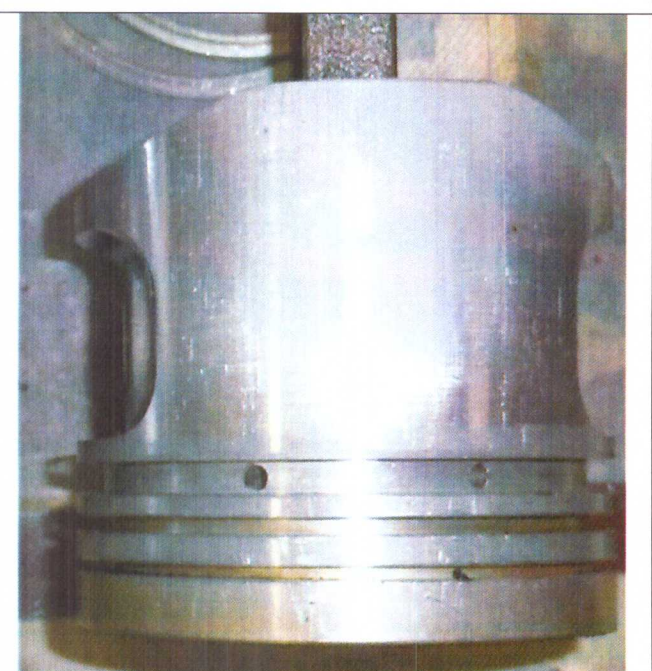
Внешний вид боковой поверхности поршня второго цилиндра по окончании длительных испытаний двигателя при работе на базовом масле Castrol EDGE с добавкой нанокompозита Amortect PROOF
